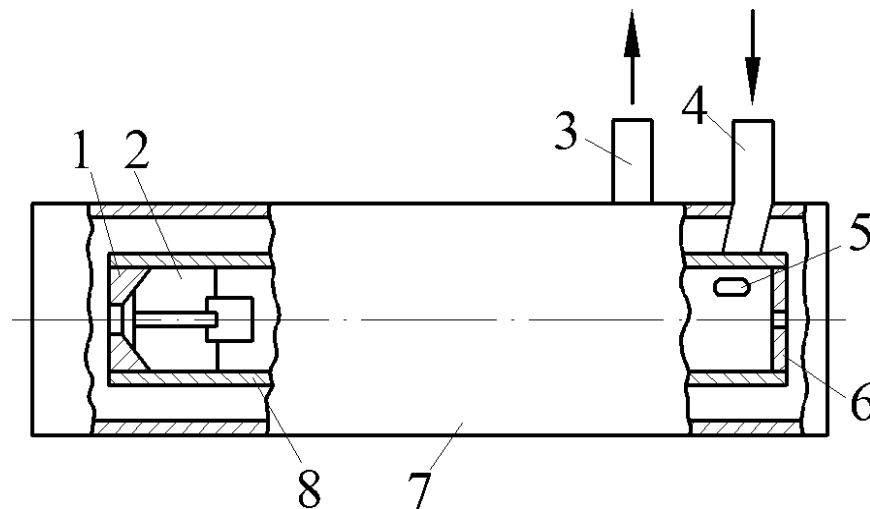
Схема будови вихрового енергоперетворювача: 1 – дросель; 2 – гальмівний пристрій; 3 – вихідний патрубок; 4 – вхідний патрубок; 5 – тангенційний отвір; 6 – діафрагма з центральним отвором; 7 – теплообмінна обойма; 8 – циліндричний корпус.
